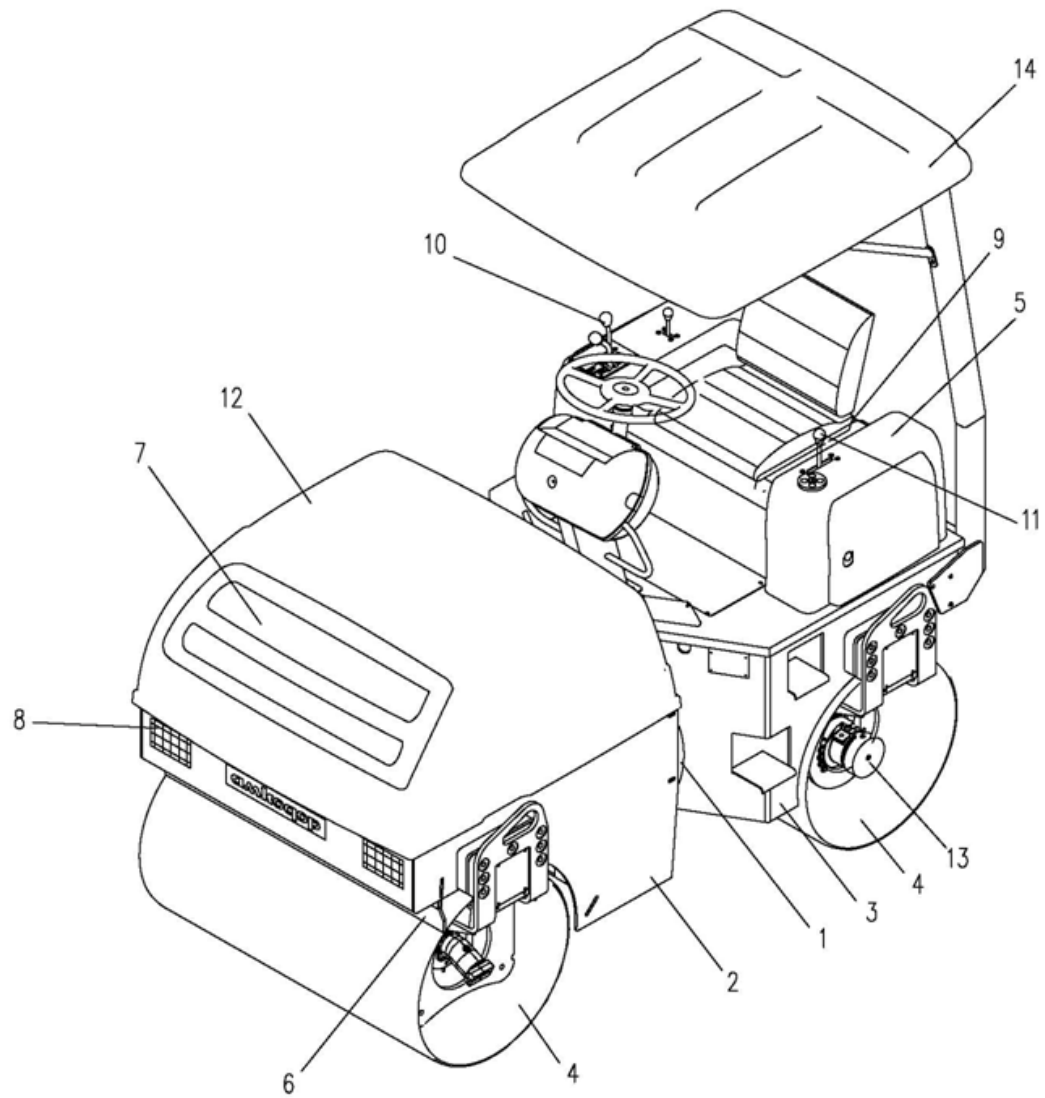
/ Fig.1 / Dib.1 6223A.00.00.000
